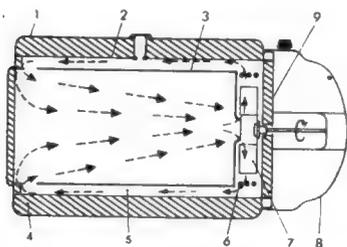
Luftführung in den runden Trockenschränken der Typenreihe U i; 1 = Außenzylinder, 2 = Mittelzylinder, 3 = Innenzylinder, 4 = Isolierung, 5 = Luftkanal, 6 = Heizungen, 7 = Turbine, 8 = Kappe, 9 = Montageplatte
